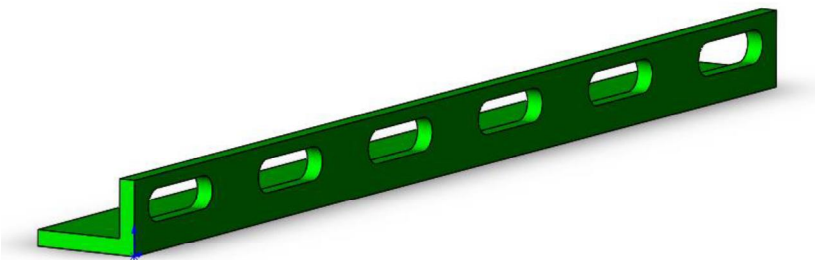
Angular de acero soldado al chasis. (Fuente: SolidWorks)
